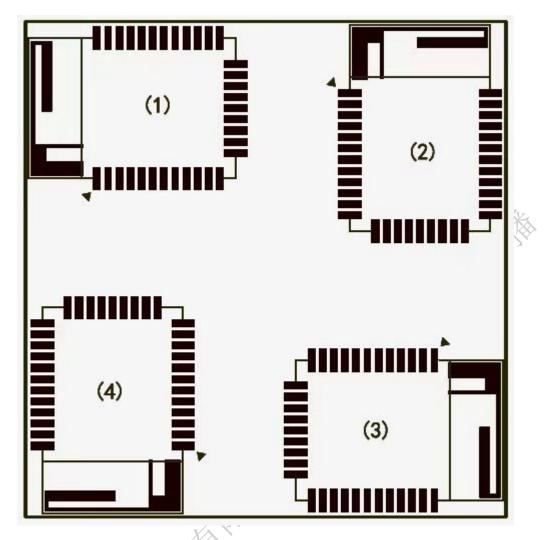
LZM1-FR16 模块在 PCB 上的 4 种摆放方式
